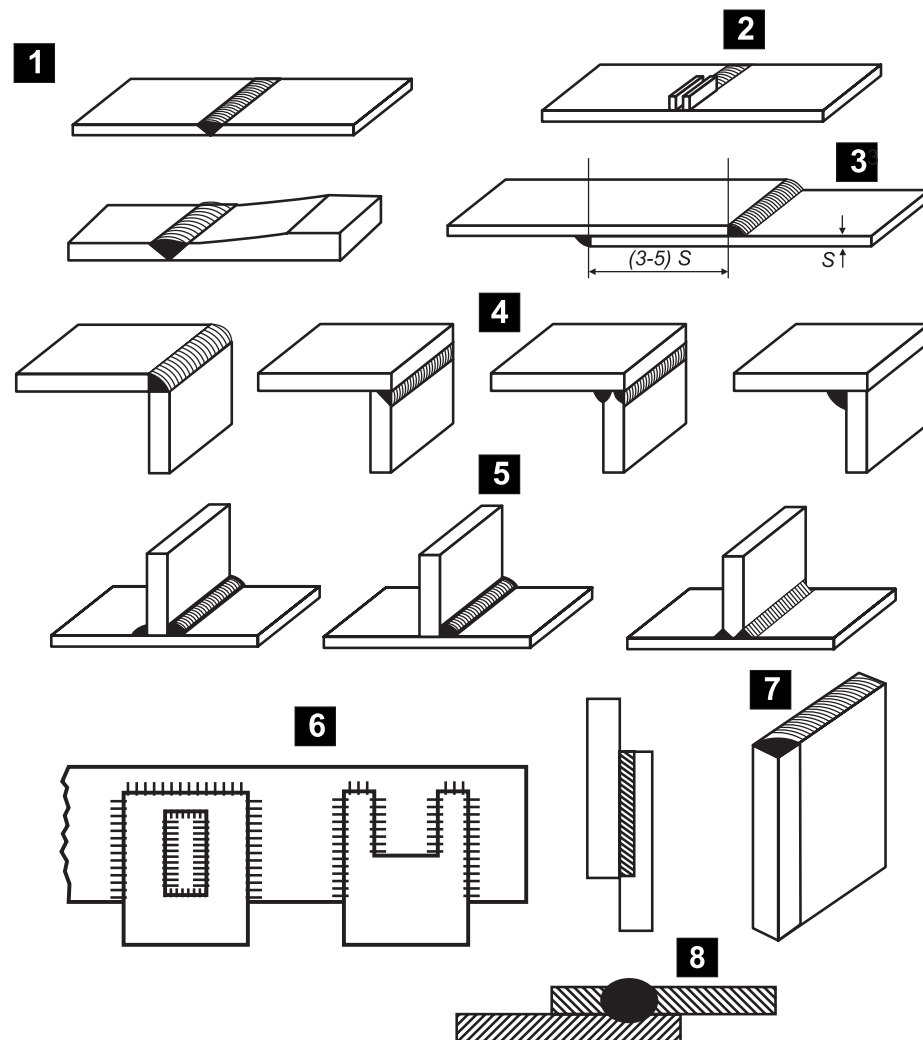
Виды сварных соединений (режим MMA)
